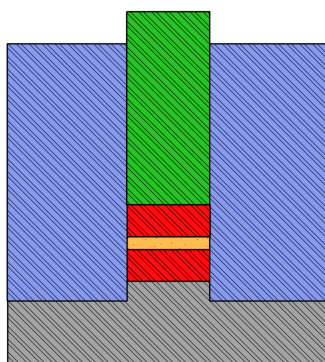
Presswerkzeug (Grundkörper, Stempel, Druckstücke, Probe, Pressplatte)
